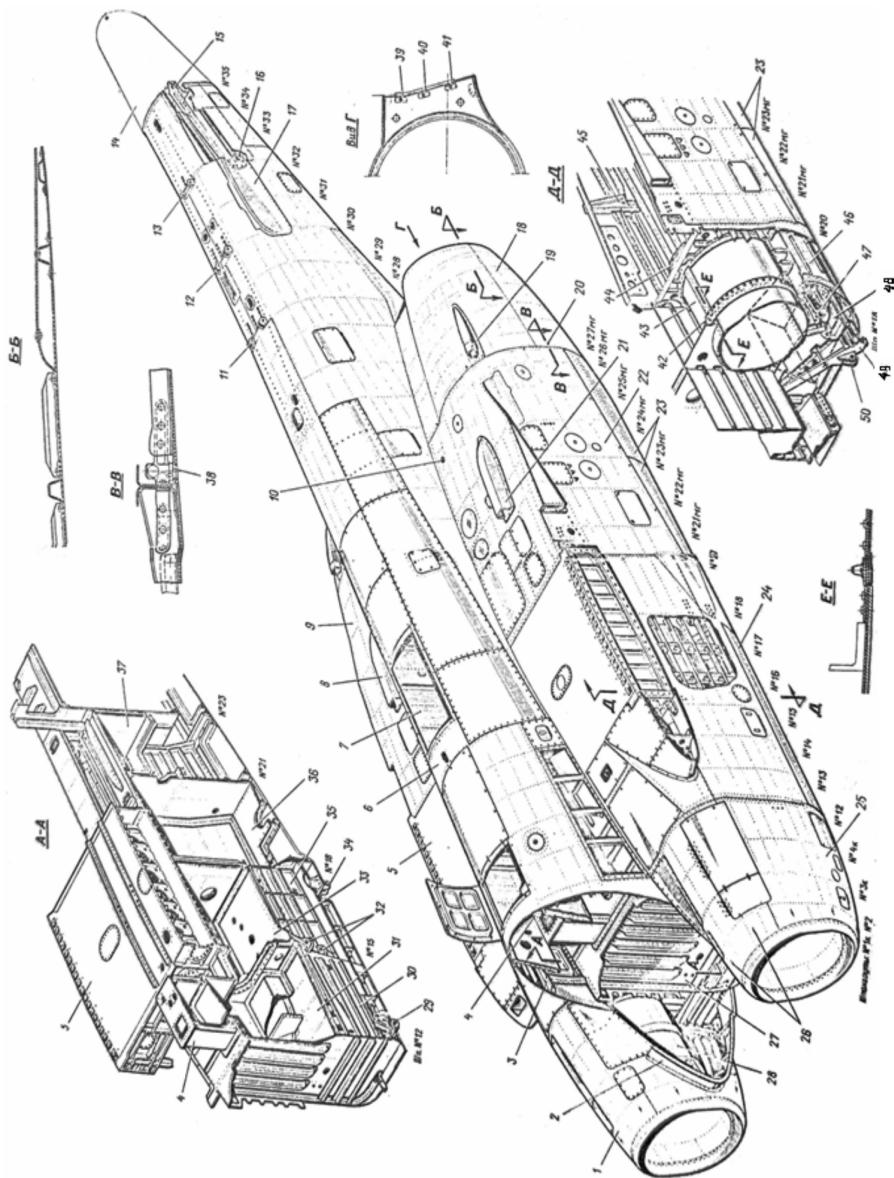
Окончание: 1 – воздухозаборник правый; 2 – клин слива; 3 – верхний лонжерон; 4 – верхняя надстройка над топливным боком; 5 – центроплан; 6 – гаргрот; 7 – вертикальная стенка гаргрота; 8, 21 – заборники воздуха для охлаждения двигателей; 9, 22 – правая и левая мотогондолы; 10 – такелажная точка; 11, 12, 13 – узлы крепления переднего, среднего и заднего лонжеронов киля; 14 – отсек парашютно-тормозной установки; 15 – кронштейн крепления тормозного парашюта; 16 – узел навески стабилизатора; 17 – зашивка; 18 – хвостовой кок; 19 – заборник воздуха для обдува генераторов двигателя; 20 – замок крепления хвостового кока; 23 – люки мотогондолы; 24 – створка ниши основной опоры самолета; 25 – воздухозаборник левый; 26 – гнезда для крепления заглушки воздухозаборника; 27– шпангоут № 12; 28 – воздушный канал воздухозаборника; 29, 34 – узлы наружной подвески; 30, 35 – вертикальные стенки, разделяющие правую и левую ниши шасси; 31 – контейнер топливного бака № 1; 32 – узел крепления складывающегося подкоса основной опоры самолета; 33 – контейнер топливного бака № 1а; 36 – контейнер топливного бака № 2; 37 – контейнер топливного бака № 2а; 38 – запорный штырь замка крепления хвостового кока; 39, 40, 41 – малогабаритные замки крепления к фюзеляжу хвостового кока по заднему торцу; 42 – лентастыковки передней и задней частей воздушного канала; 43 – воздушный канал двигателя; 44 – опорное резиновое кольцо на стыке с двигателем; 45 – кронштейн подвески двигателя; 46 – подканальный топливный бак (2к); 47 – верхний узел крепления стойки основной опоры самолета; 48 – бимс; 49 – нижний узел крепления стойки основной опоры самолета; 50 – узел крепления тяги отвала основной опоры самолета
